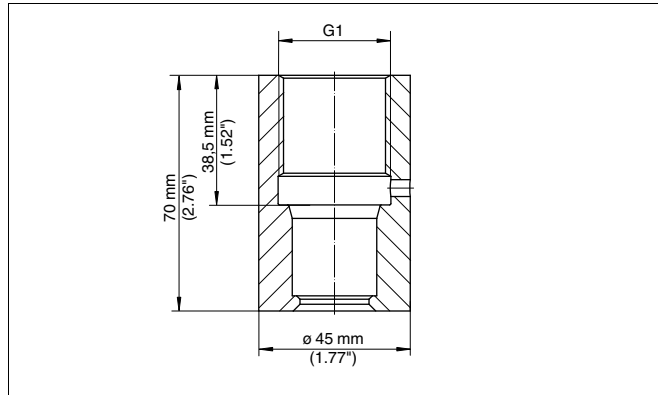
Maße Einschweißstutzen G1" geeignet für PASVE
